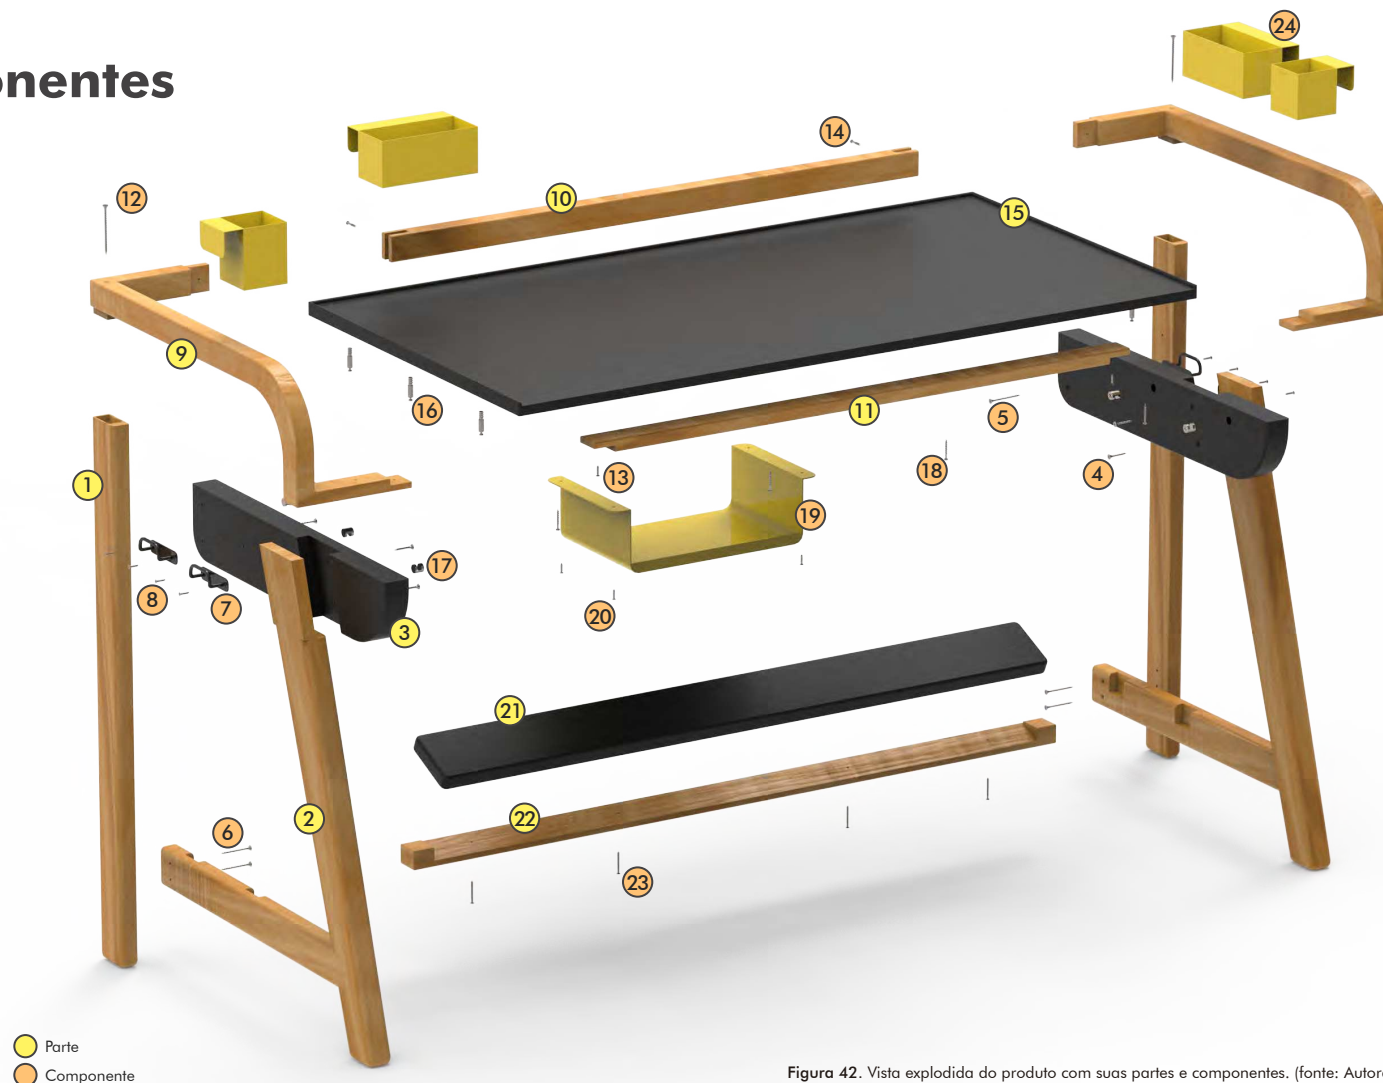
Vista explodida do produto com suas partes e componentes. (fonte: Autoral)
